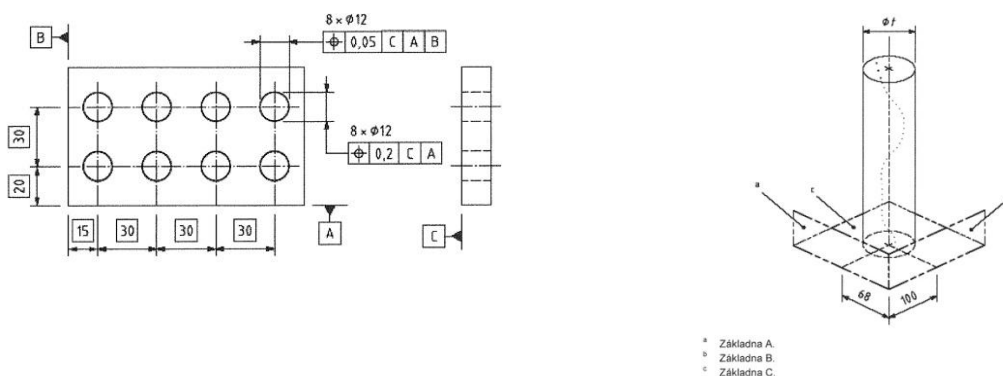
Označení a vysvětlení geometrické tolerance polohy bodu [4]
